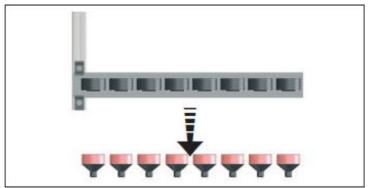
spingere la placchetta di serraggio (c) verso il basso. Stringere saldamente entrambe le viti M8.
